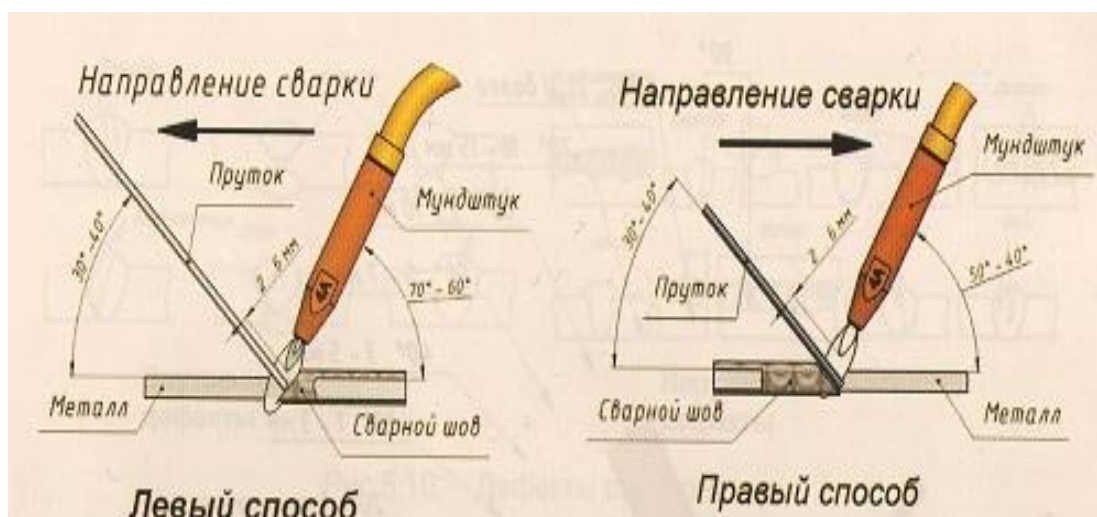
Способы выполнения газовой сварки.
